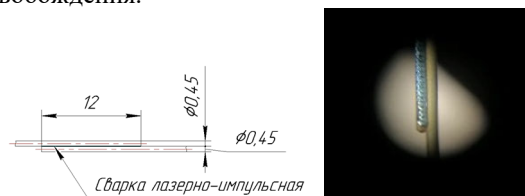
Фото под микроскопом места приварки лазерно-импульсной сваркой нитинола с нитинолом и схемы приваривания
